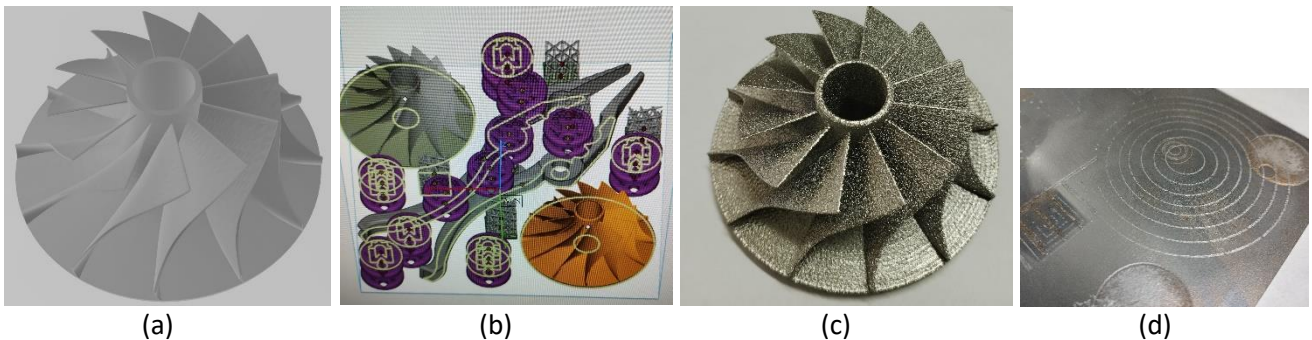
modello CAD (a), scena di stampa (b) turbina (c), piatto di stampa(d)
